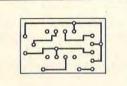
Layout im Maßstab 1:1 (Lötseite)
